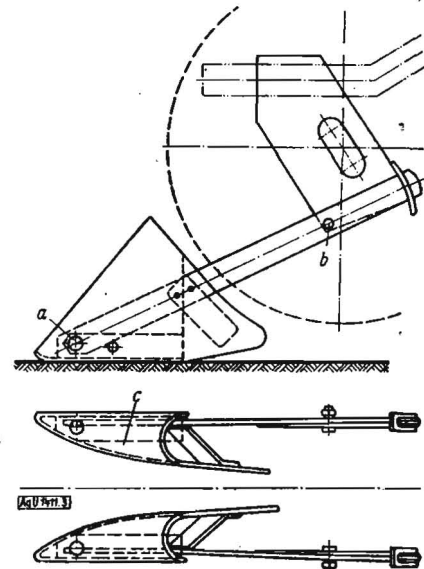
Schwimmender Krautheber. a Kugelgelenk, b Gelenk, c Mantelblech
